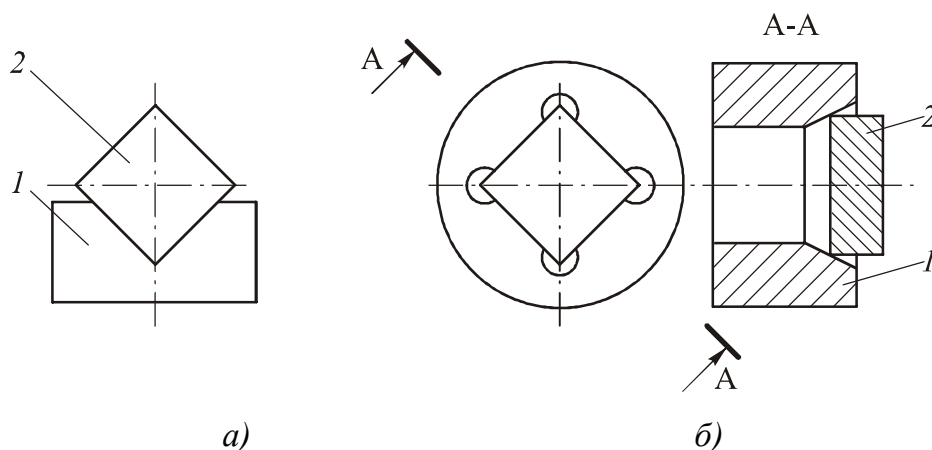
Способы базирования пластин на станке с ЧПУ:
